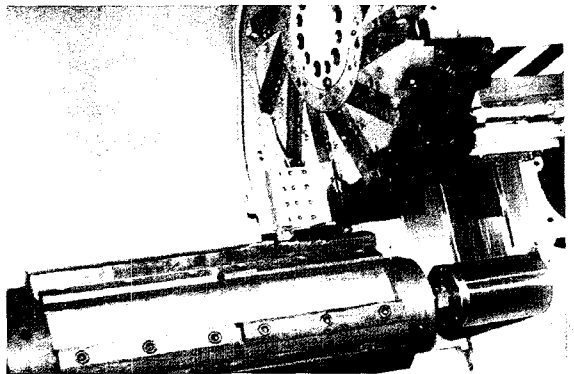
Drehmaschine DFS 2/2 CNC H-645 mit Kistler-Schnittkraftmesser
